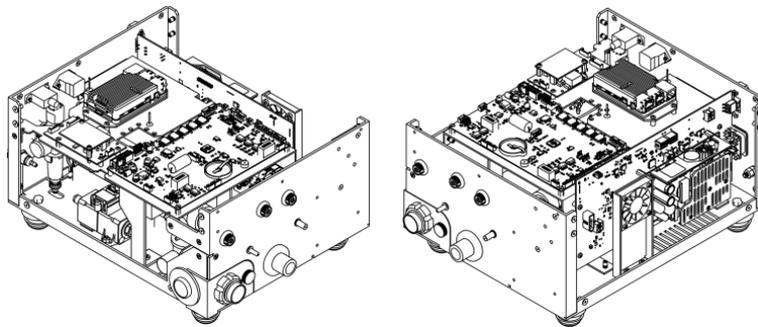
Diseño de la base principal y su ensamble con la base de tarjetas.
